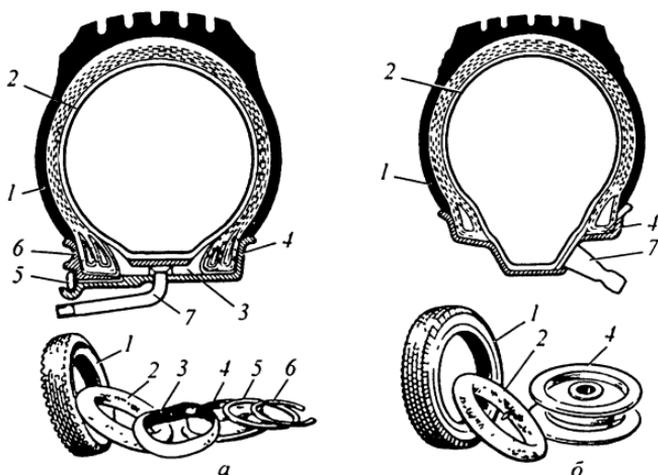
Камерные шины: *а* — для плоского обода; *б* — для глубокого обода; 1 — покрышка; 2 — камера; 3 — ободная лента; 4 — диск колеса; 5 — бортовое кольцо; 6 — замочное кольцо; 7 — вентиль
